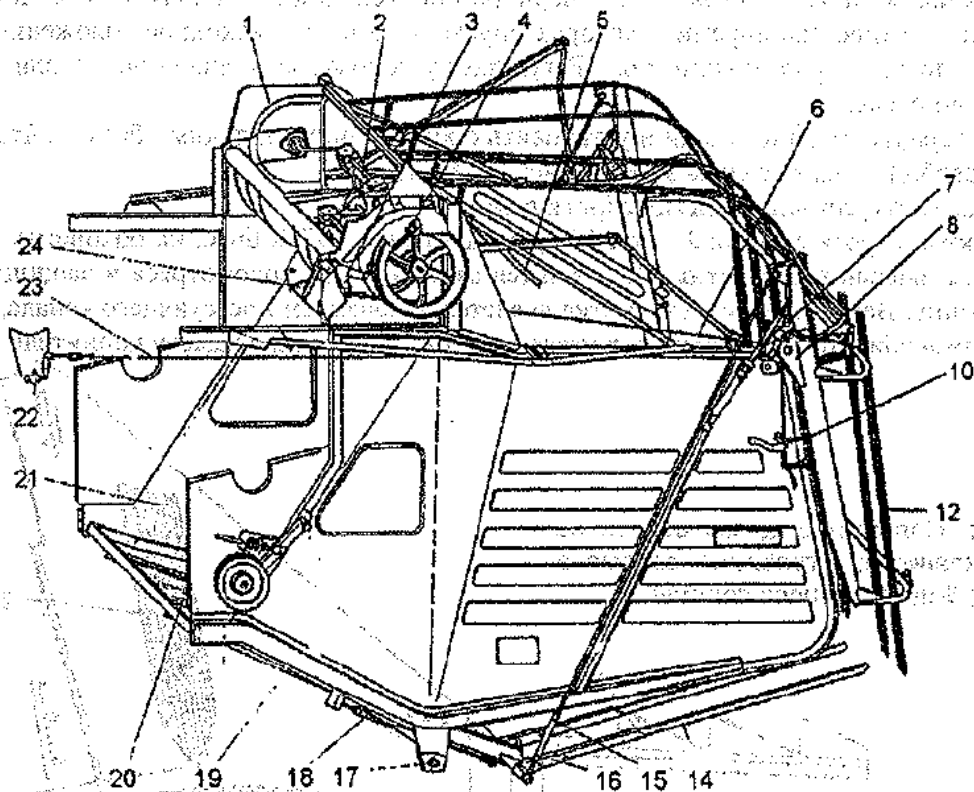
Копнитель: 1-капот; 2-соломонабиватель; 3-механизм сбрасывания копны; 4-гидроцилиндр открытия копнителя; 5-сигнализатор; 6-тяга механизма сбрасывания; 7-гидроцилиндр закрытия копнителя; 8-клапан копнителя; 9-поперечина клапана верхняя; 10-сигнализатор открытия копнителя; 12-планка вертикальная; 14-палец днища; 15-гайка стяжная; 16-звено пальца днища промежуточное; 17-ось крепления днища; 18-пружина днища; 19-боковина левая; 20-днище; 21-боковина правая; 22-гидрораспределитель копнителя; 23-тяга гидрораспределителя; 24-щиток сброса соломы
